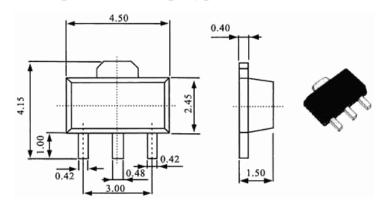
Зовнішній вигляд корпусу типу SOT89
